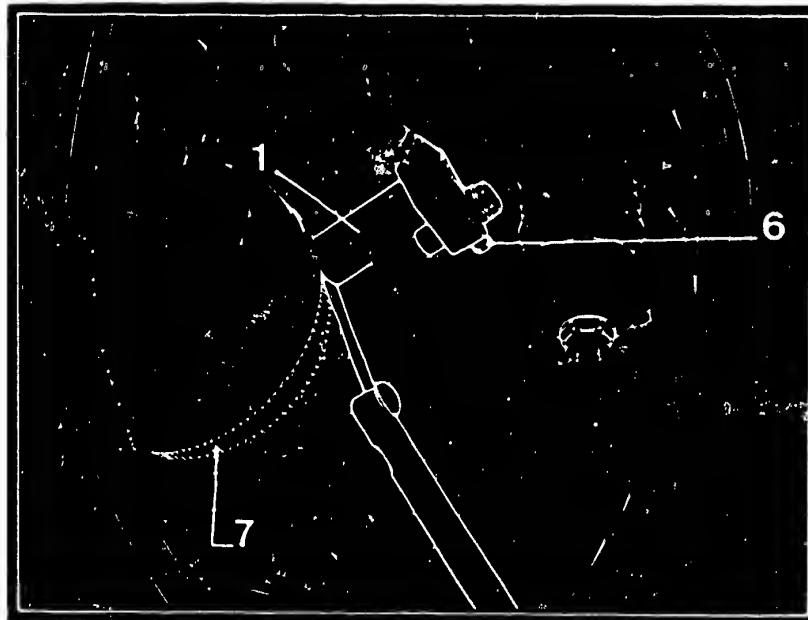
Das Einstellen des Drehzahlensensors an einem Vorderrad. 1 Sensor – 6 Fixierschraube – 7 Zahnkranz.
